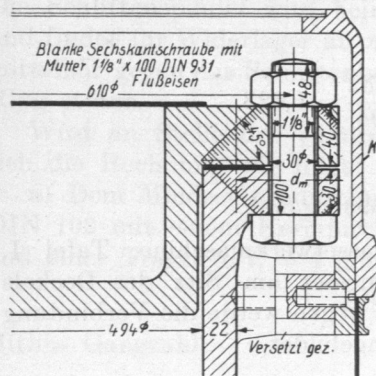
Flanschverbindung mittels Durchsteckschrauben, M. 1:4.
